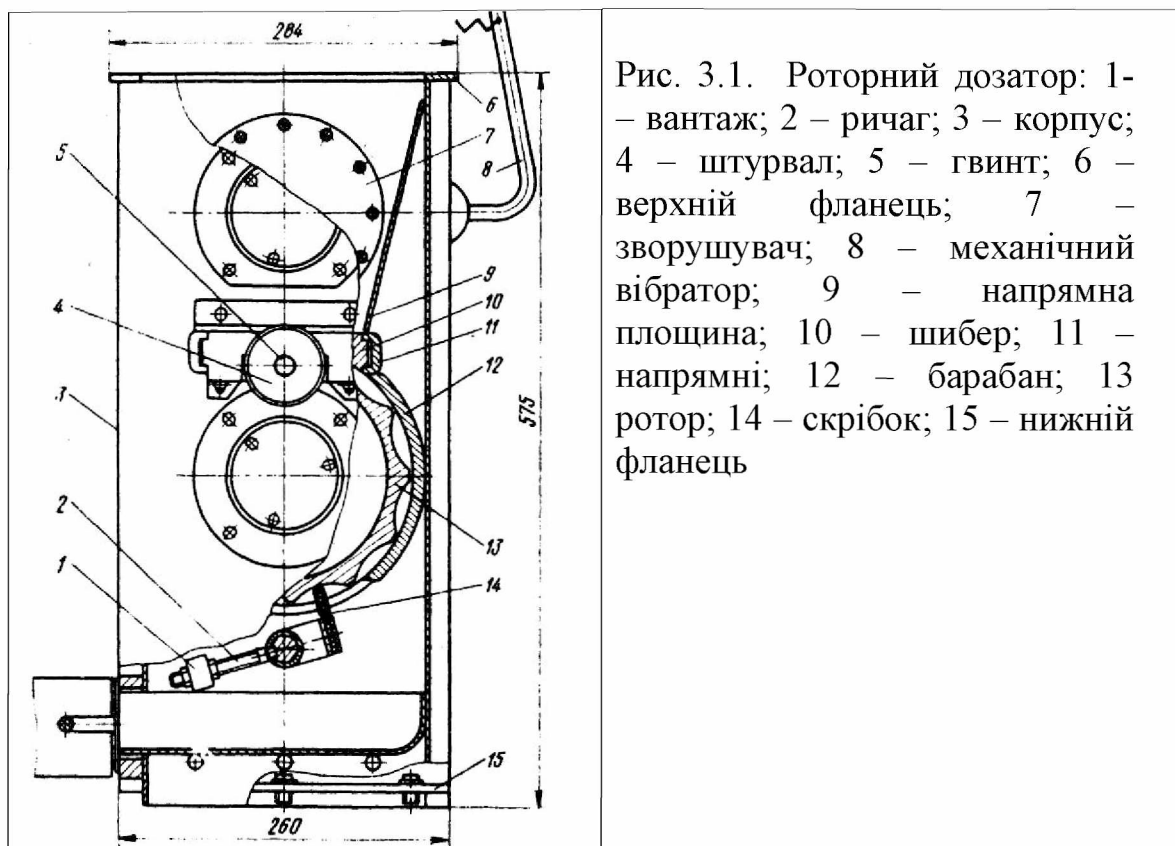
Роторний дозатор: 1 – вантаж; 2 – ричаг; 3 – корпус; 4 – штурвал; 5 – гвинт; 6 – верхній фланець; 7 – зворушувач; 8 – механічний вібратор; 9 – напрямна площа; 10 – шибер; 11 – напрямні; 12 – барабан; 13 – ротор; 14 – скрібок; 15 – нижній фланець
